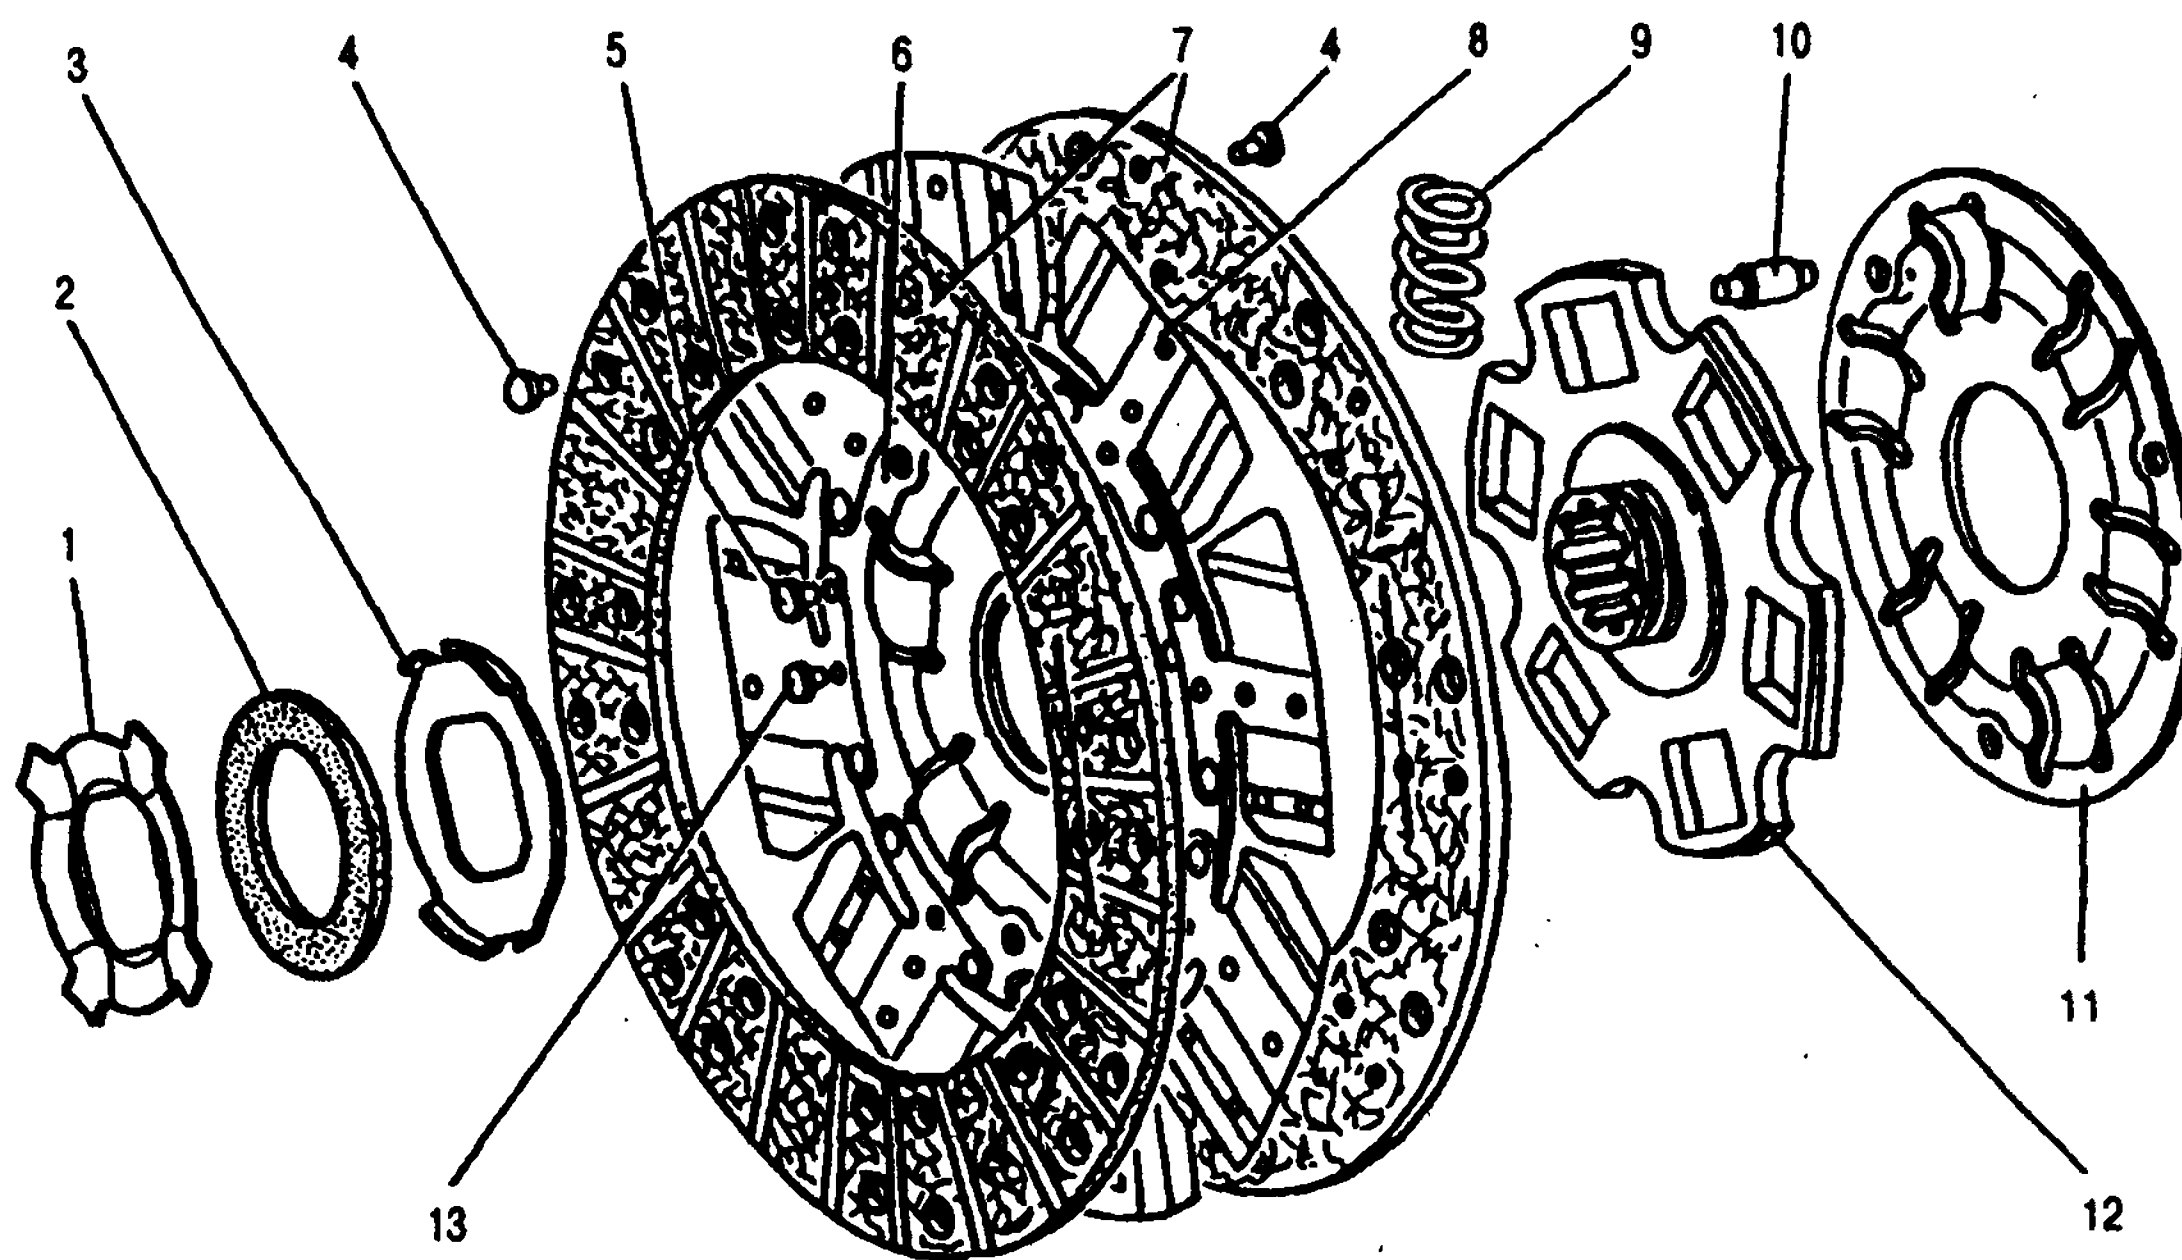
Ведомый диск сцепления: 1 - нажимная пружина; 2 - теплоизолирующая шайба; 3 - фрикционная шайба; 4, 5 - заклепки; 6, 11 - диски; 7 - фрикционные накладки; 8 - пластинчатая пружина; 9 - пружина демпфера; 10 - палец; 12 - ступица; 13 - балансировочный грузик
